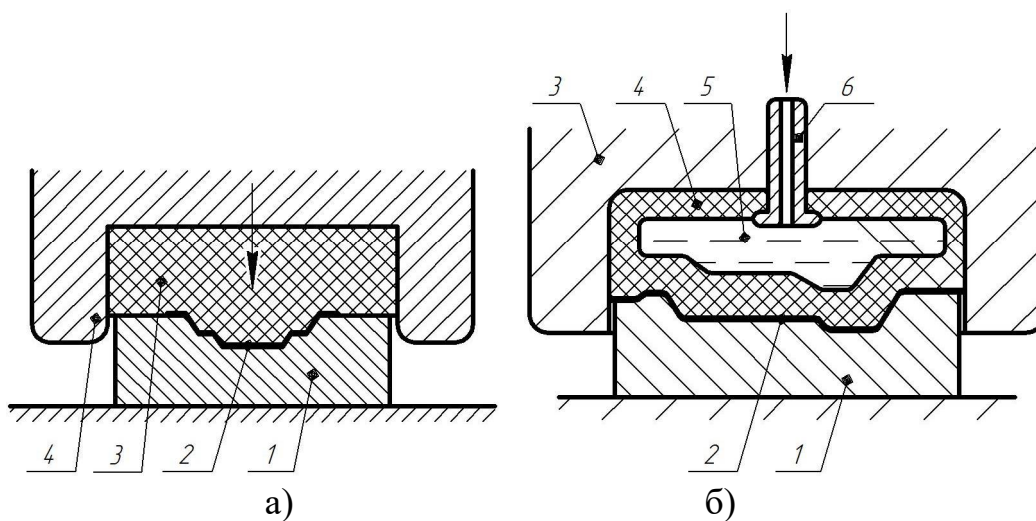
Схеми холодного листового штампування: а – гумою: 1 – матриця; 2 – заготівка; 3 – гумова подушка; 4 – обойма; б – гідравлічного: 1 – матриця; 2 – заготівка; 3 – обойма; 4 – гумовий мішок; 5 – робоча рідина; 6 – трубка для підведення рідини
